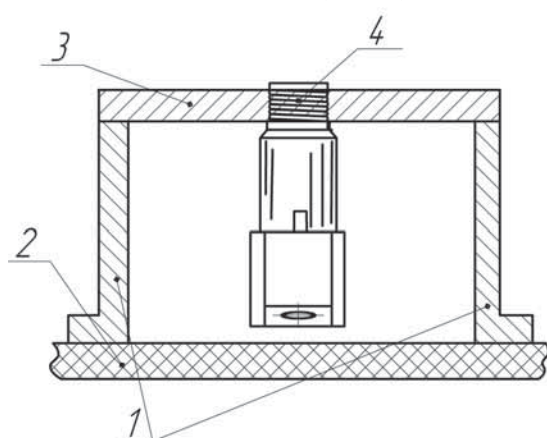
Одностоечное приспособление для шлифования торца корпуса форсунки:
